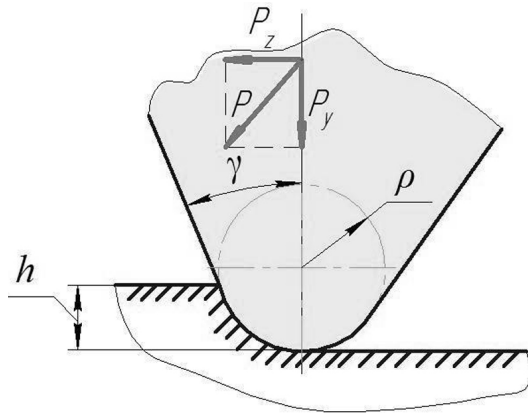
Схема силового взаимодействия единичного зерна хон-бруска мультиинденторного инструмента с обрабатываемой поверхностью: h – глубина внедрения; ρ – радиус округления режущего элемента зерна
